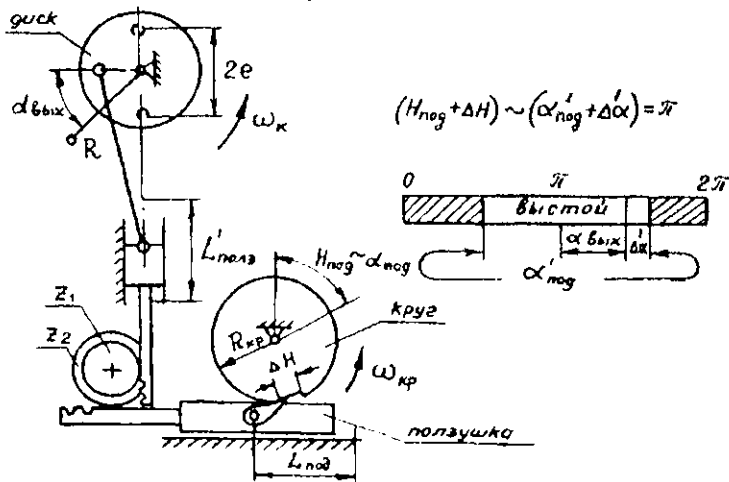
Поворотный круг с приводом от главного вала КИМ
